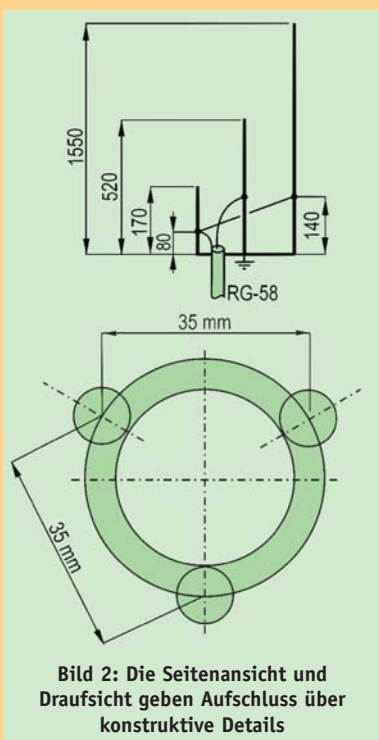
Die Seitenansicht und Draufsicht geben Aufschluss über konstruktive Details
